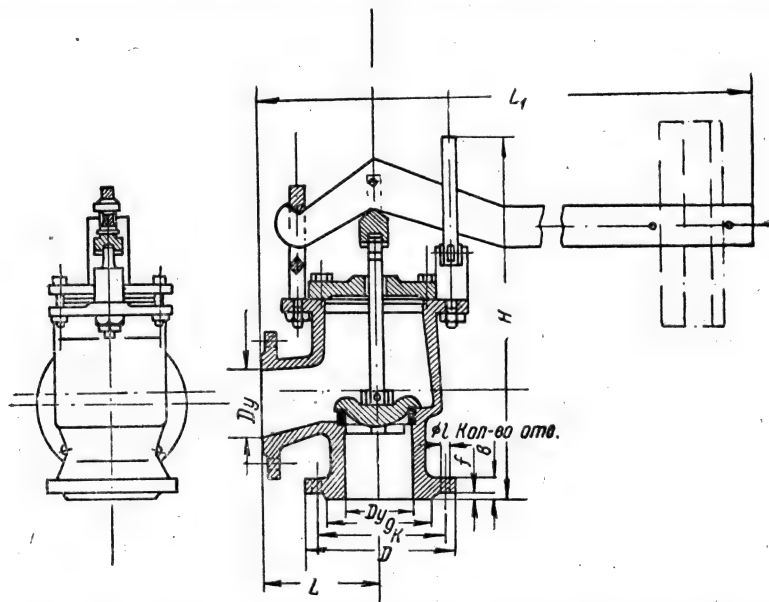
Клапан предохранительный неполноподъемный однорычажный 17ч3бр.
